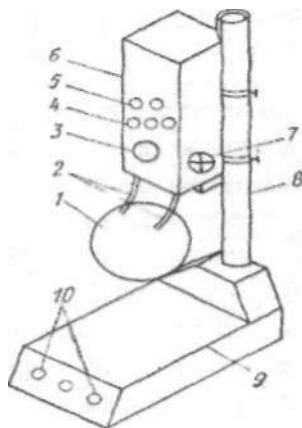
Схема сварочной машины специальной конструкции
